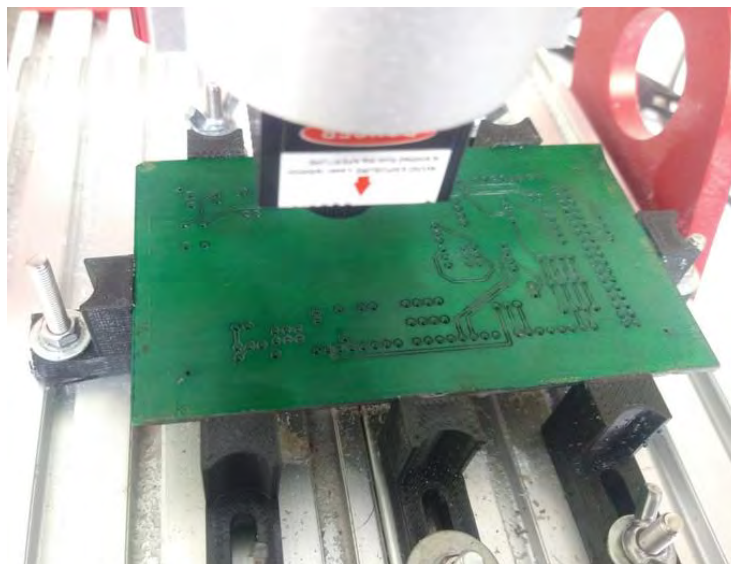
Montaje de placa en CNC para Proceso de corte laser
